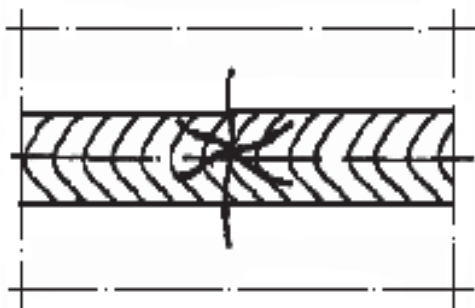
Схематичное изображение радиальной трещины сварного соединения
